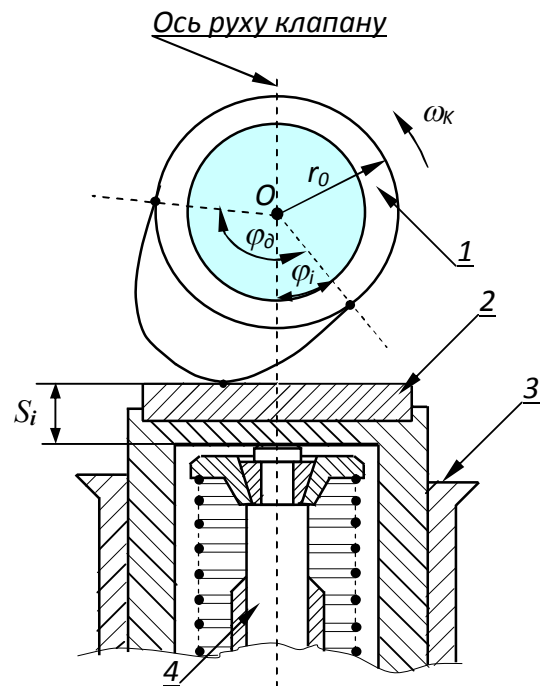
Схема КМГР дизеля типу ЧН 8,8/8,2: 1 – газорозподільний кулачок; 2 – плоский штовхач; 3 – напрямна; 4 – клапан
